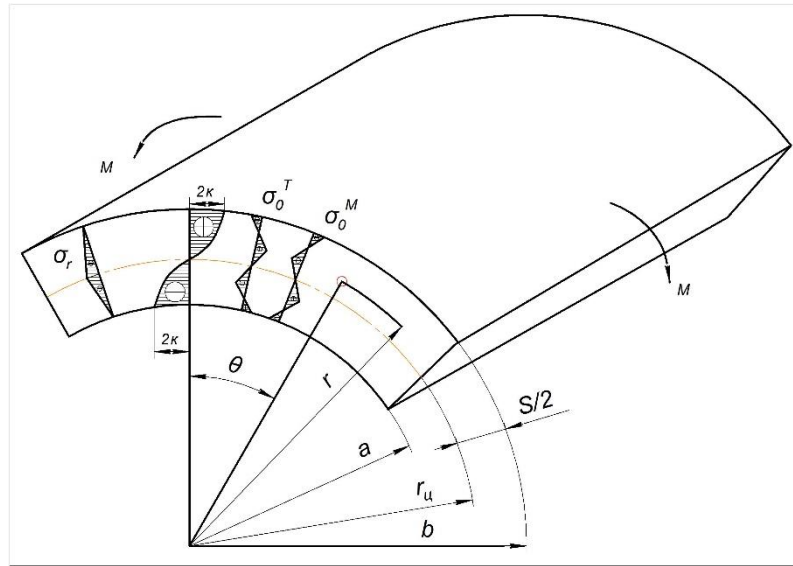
Схема формування листової заготовки та епюри розподілу напружень по товщині листа
